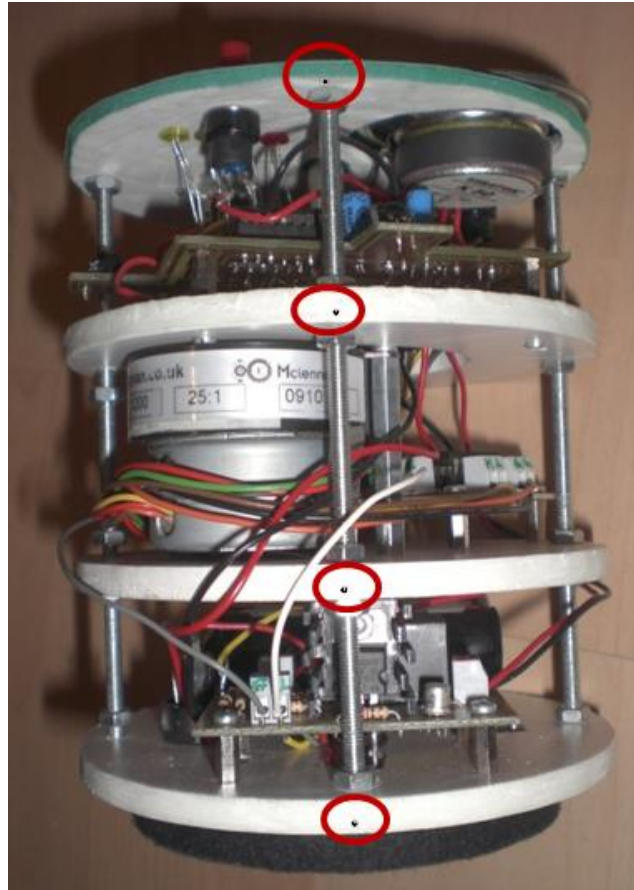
71: Detalle de las marcas en las plantas para colocar la estructura fija
